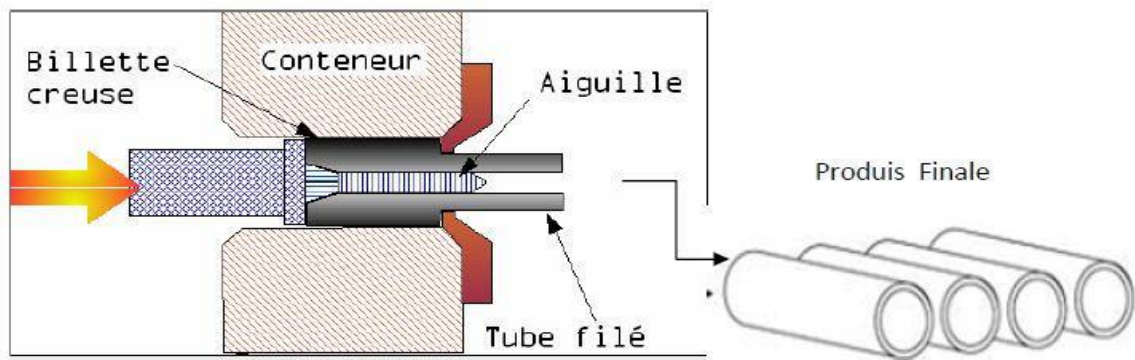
Obtention des tubes sans soudure [HAD 13]
